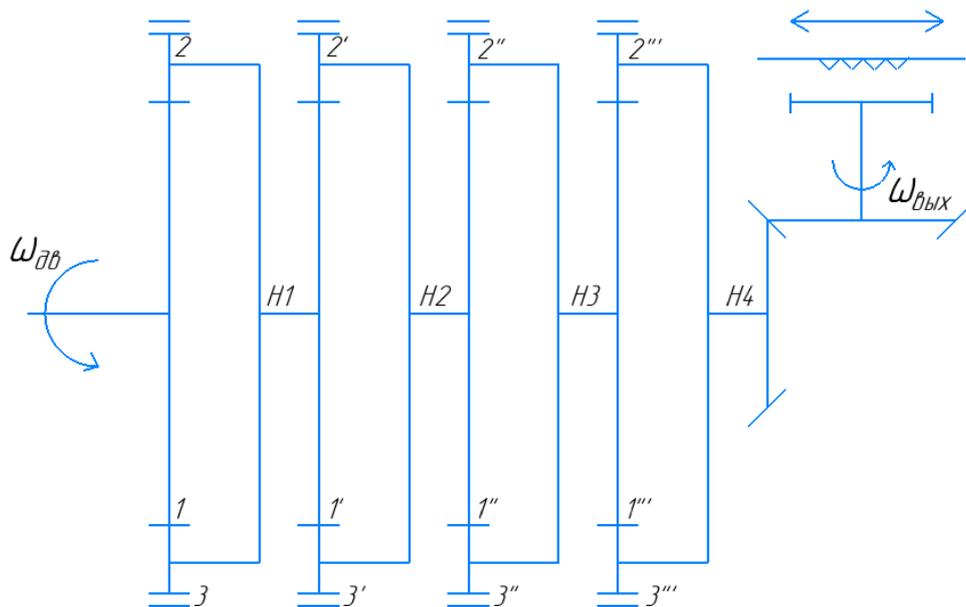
Кинематическая схема механической передачи привода активного вариатора:
